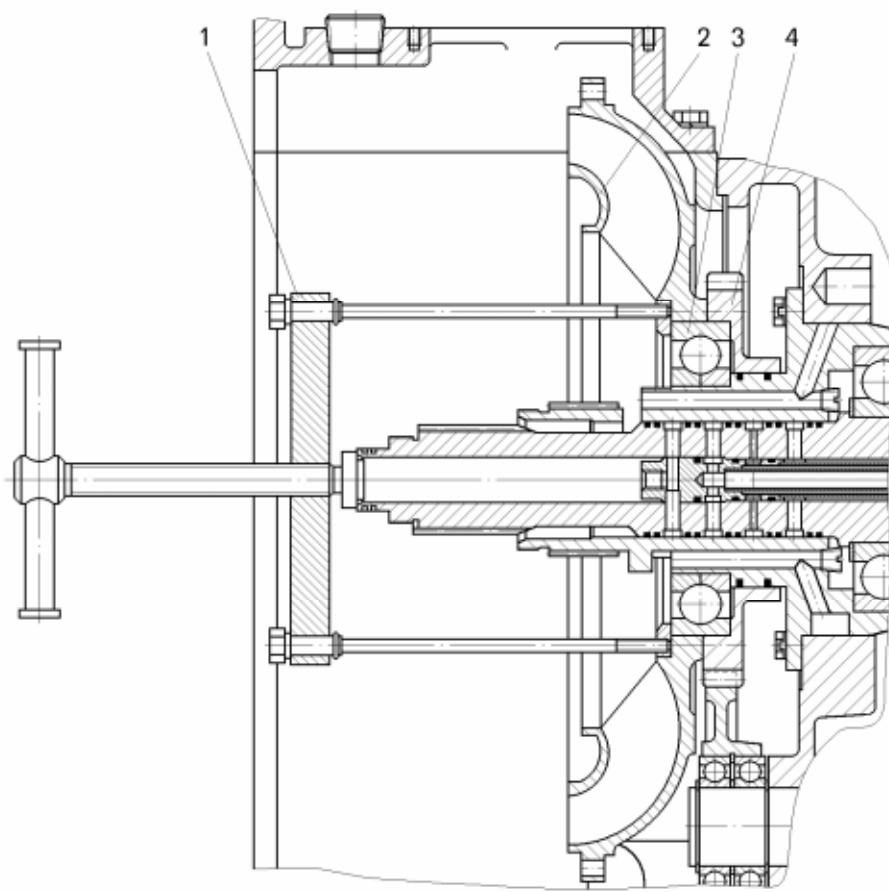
Снятие насосного колеса с подшипником и ведущей шестерни привода насоса:
